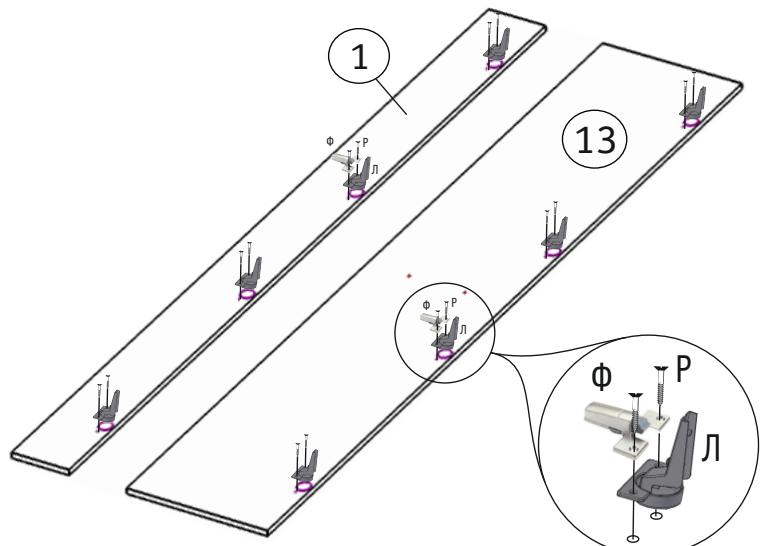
Установите петли на фасадах, в одну из чашек петли на каждом фасаде установите по демпферу для плавной доводки. Закрепите ручку на фасаде 13. Совместите петли на фасадах с ответными планками на боковинах и закрепите фасады. Отрегулируйте петли и демпфера (см. рис. 11,12)
